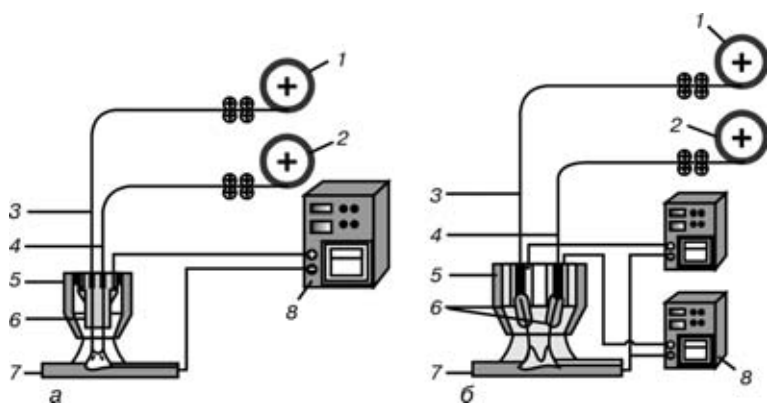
Схема сварки МИГ двумя проволоками: а — сварка МИГ спаренными электродами; б — последовательными дугами; 1, 2 — механизм подачи проволоки; 3, 4 — соответственно первая и вторая проволока; 5 — газовое сопло; 6 — мундштук; 7 — обрабатываемая деталь; 8 — источник питания
